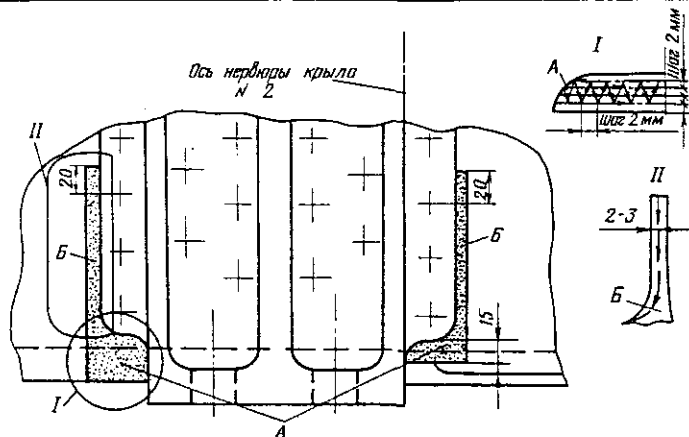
Стенка нижнего пояса заднего лонжерона центроплана в районе окончания лапки кронштейна 24-1020-5 у нервюры № 2 крыла (вид снаружи):
